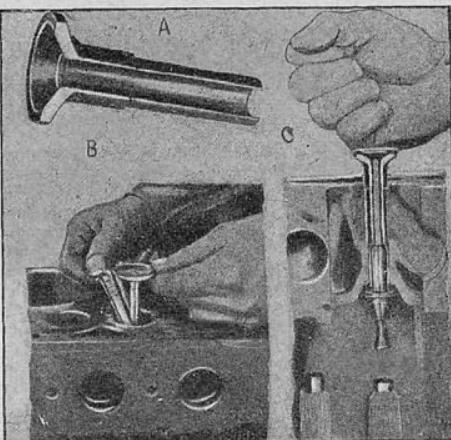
Удаление направляющей втулки стержня клапана двигателя Форд
